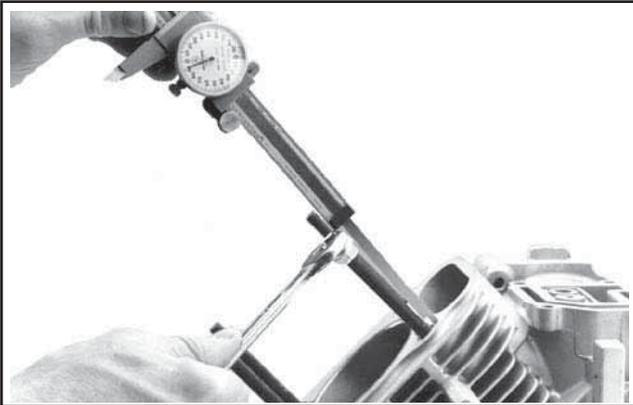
Installation de goujons d'assemblage neufs à la hauteur recommandée.
